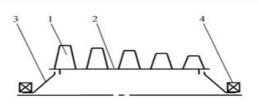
Ротор ОК барабанного типа: 1 – рабочая лопатка; 2 – цилиндрический барабан; 3 – цапфа; 4 – подшипник
